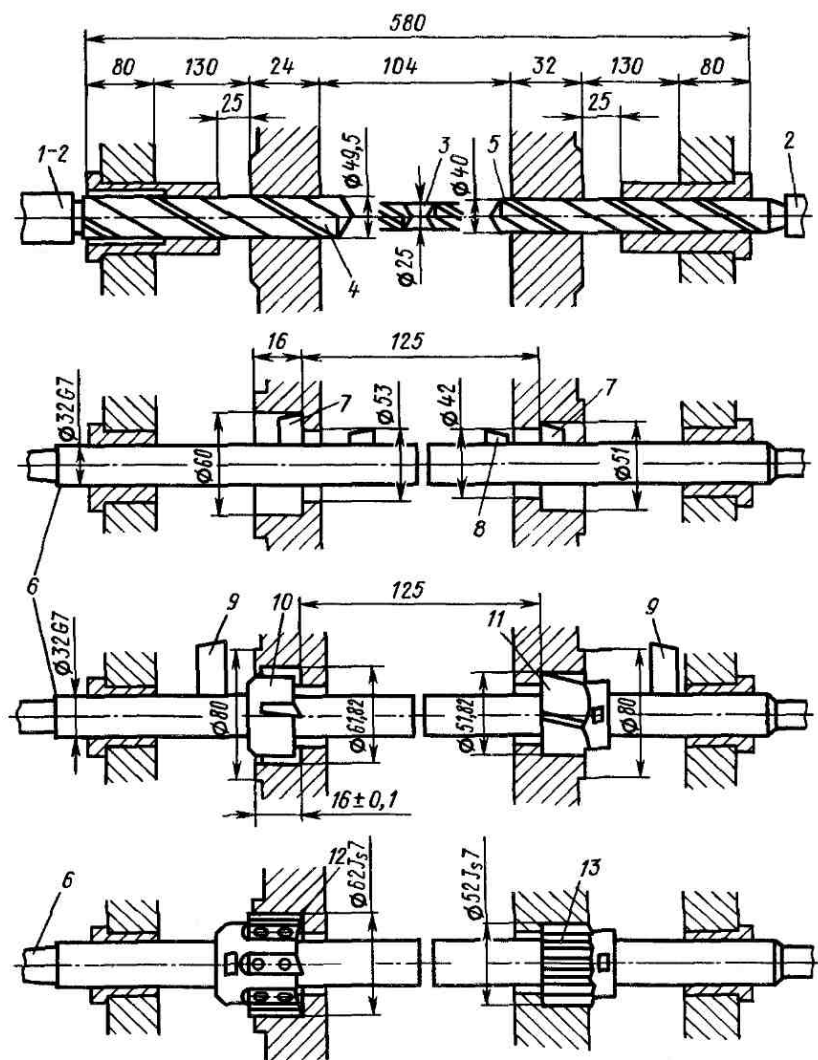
Обработка отверстий $\varnothing 52Js7$, $62Js7$
